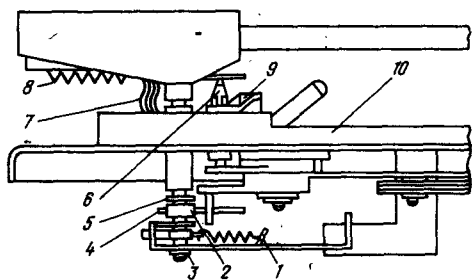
Механизм звукоснимателя ЭПУ:
